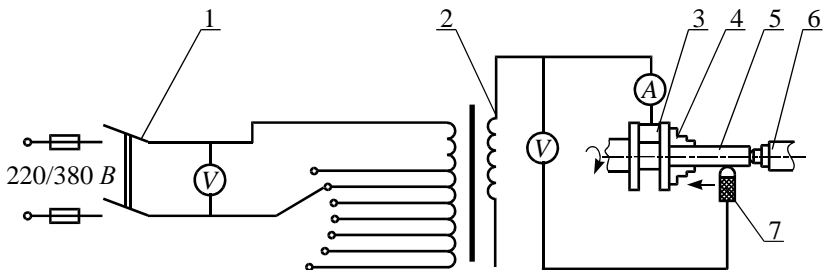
Схема ЕМО деталі на токарному верстаті:
